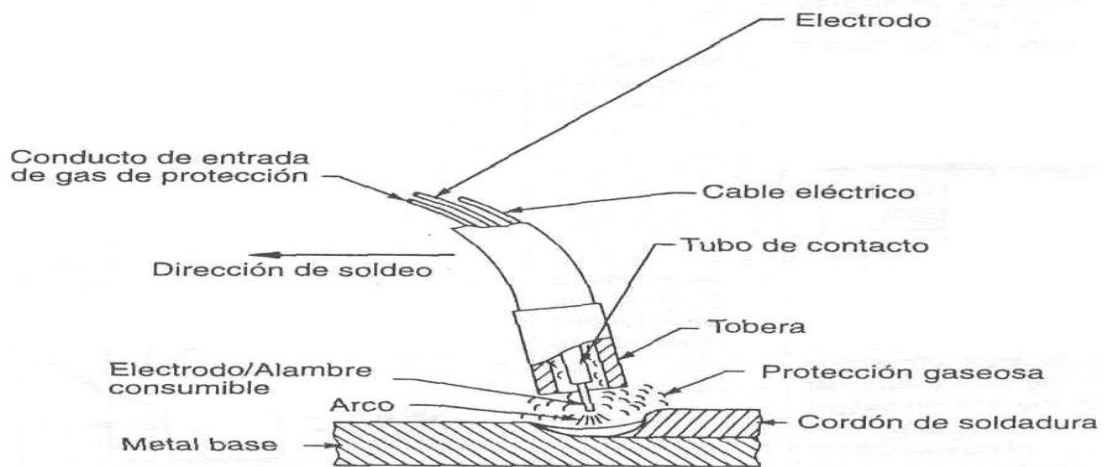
Principio de operación soldadura GMAW (Figura tomada del "Instituto Argentino de Siderurgia")
